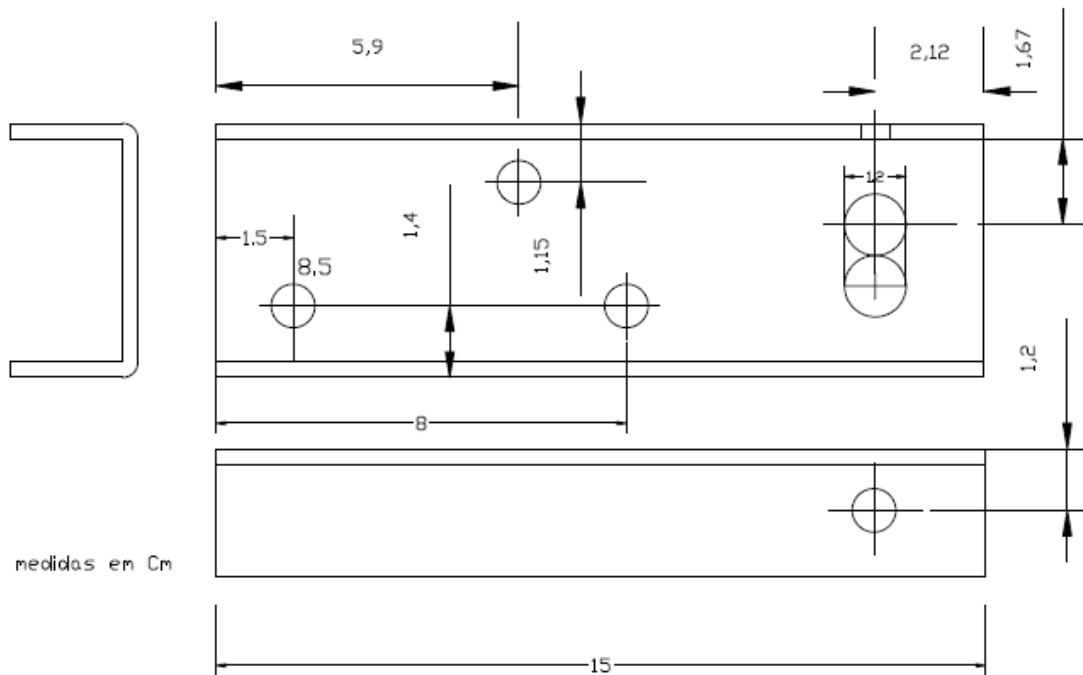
Desenho do pormenor do suporte sem rolo
